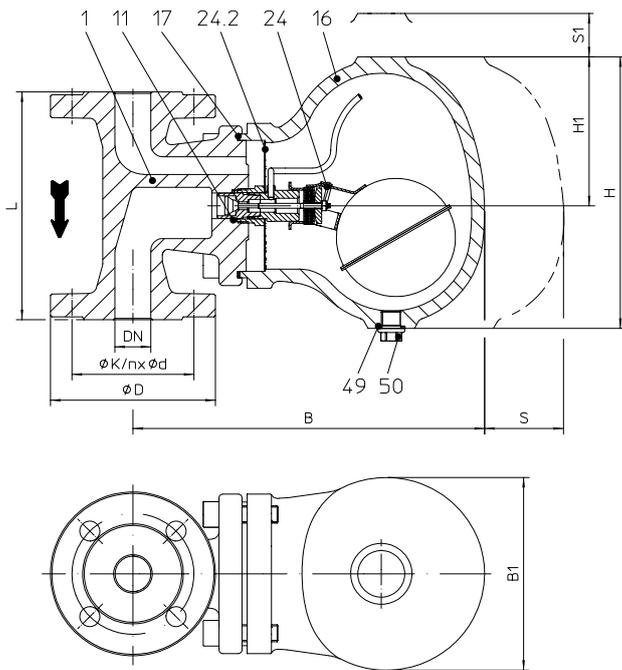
1 mit Flanschen - vertikale Einbaulage
